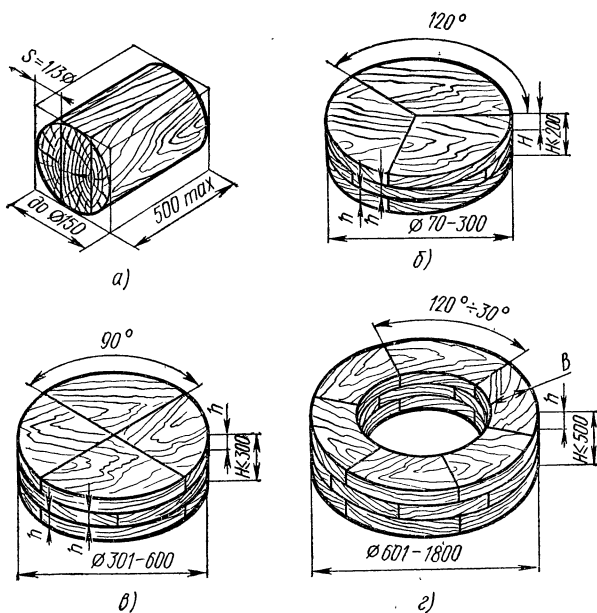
Дисковые и кольцевые заготовки (а—г)
